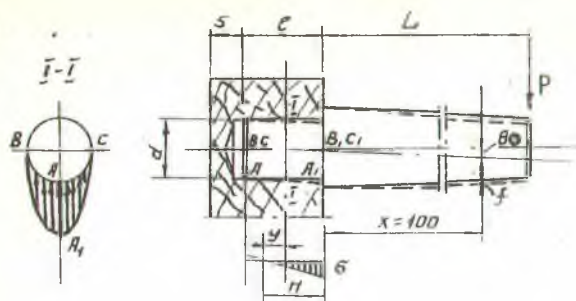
Схема шипового соединения передней ножки с царгой стула.
